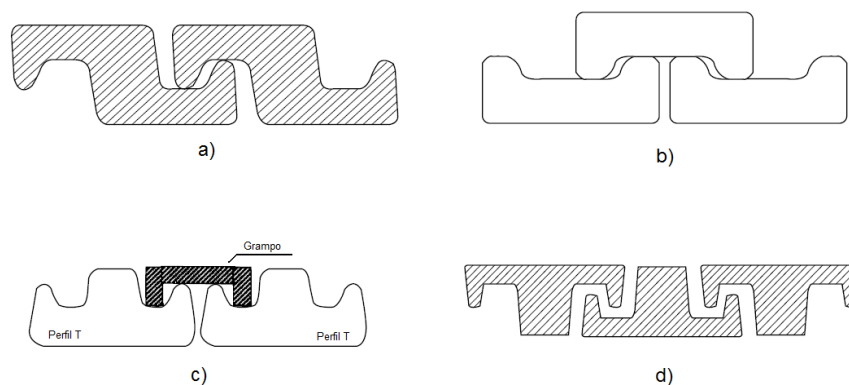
Perfis para a armadura de pressão: a) perfil Z, b) perfil C, c) perfil T (grampo ligando os perfis) e d) perfil T (API RP 17B, 2002, p. 13).
